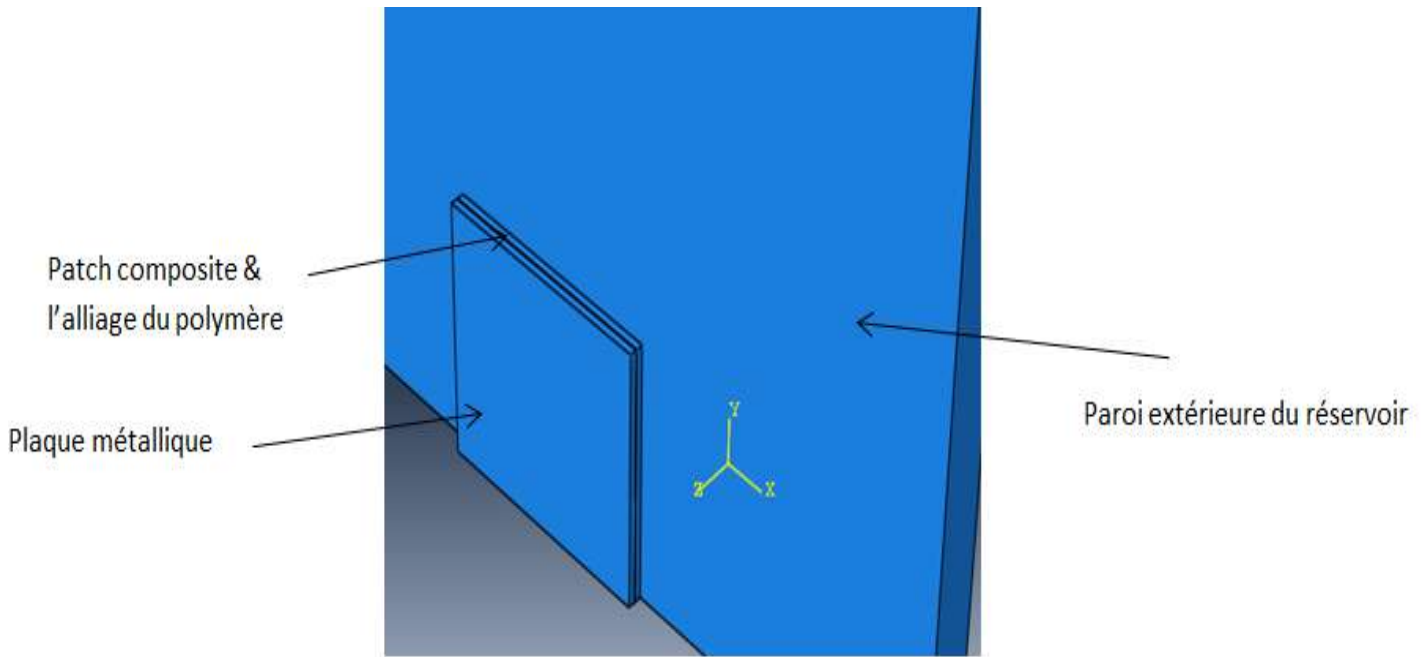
Réparation de la fissure par assemblage (soudage à froid)
